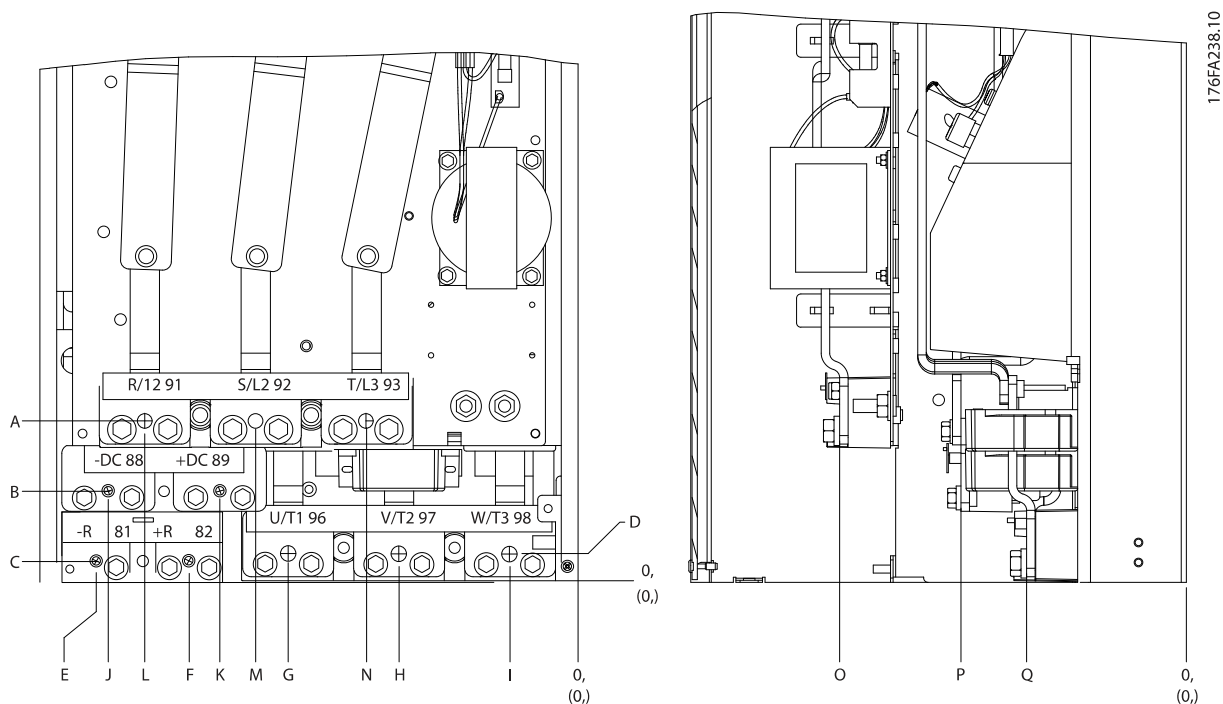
Spațiul din fața tipului de carcasă IP21/IP54, dimensiunea de carcasă F4
